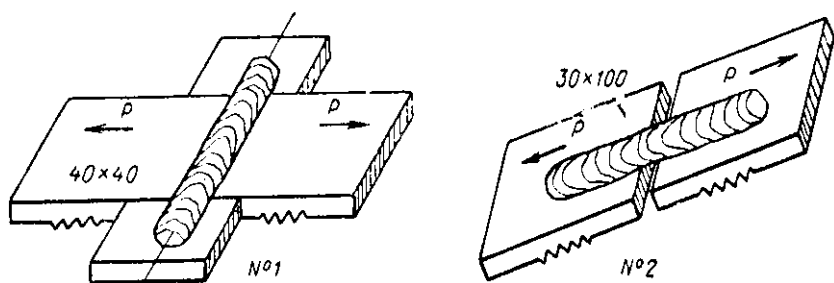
Схема образцов для испытаний на горячие трещины:
